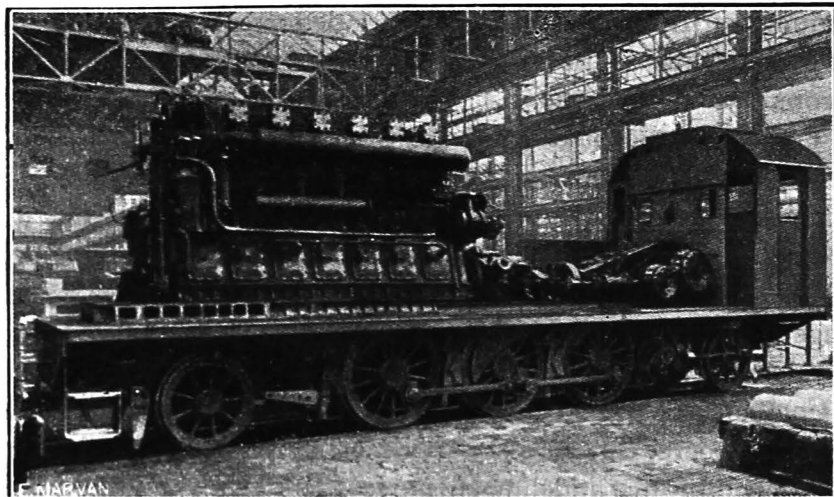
Locomotivă Diesel 600 C. P. cu transmisie prin angrenaje.
